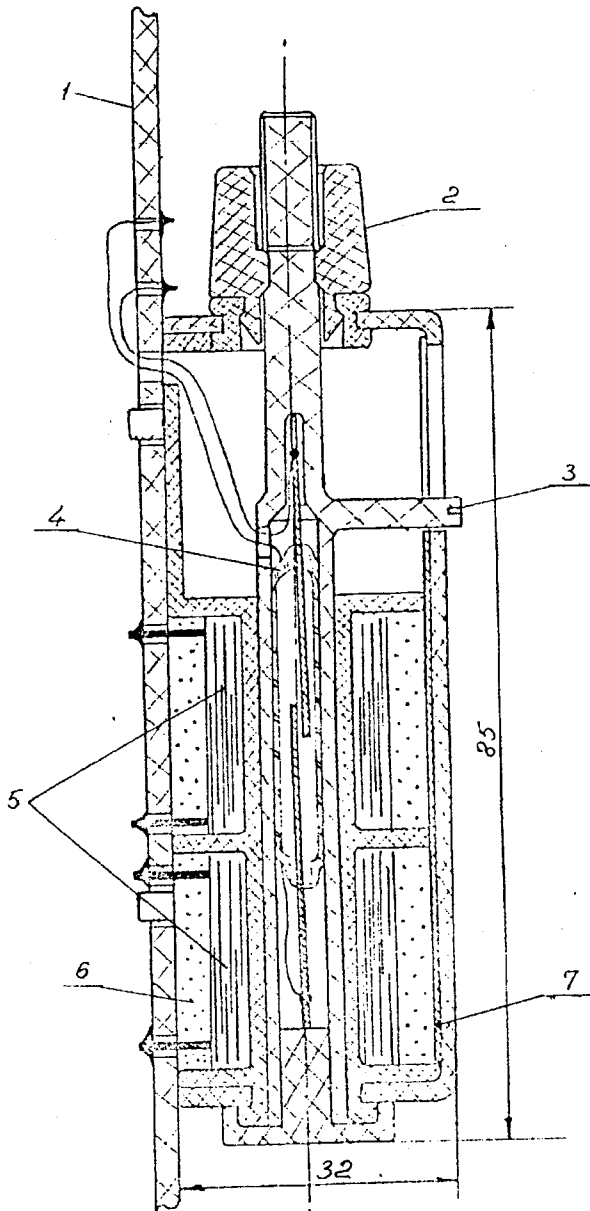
Конструкция интерфейса катушечного типа: 1 — плата печатания; 2 — ручка регулировки тока срабатывания; 3 — стрелка-указатель; 4 — геркон; 5 — катушка; 6 — заливочная масса (стеарин, эпоксидный компаунд и т.п.); 7 — ферромагнитный экран
